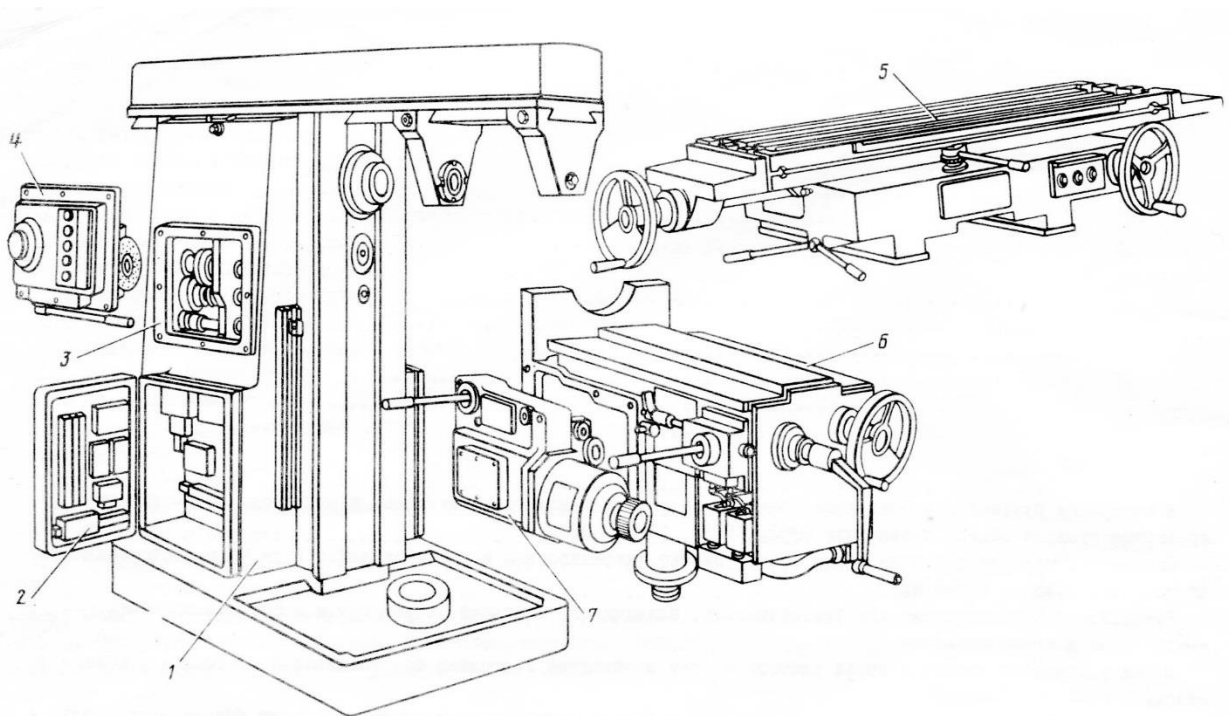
Основні конструкційні модулі горизонтального консольно - фрезерного верстата
